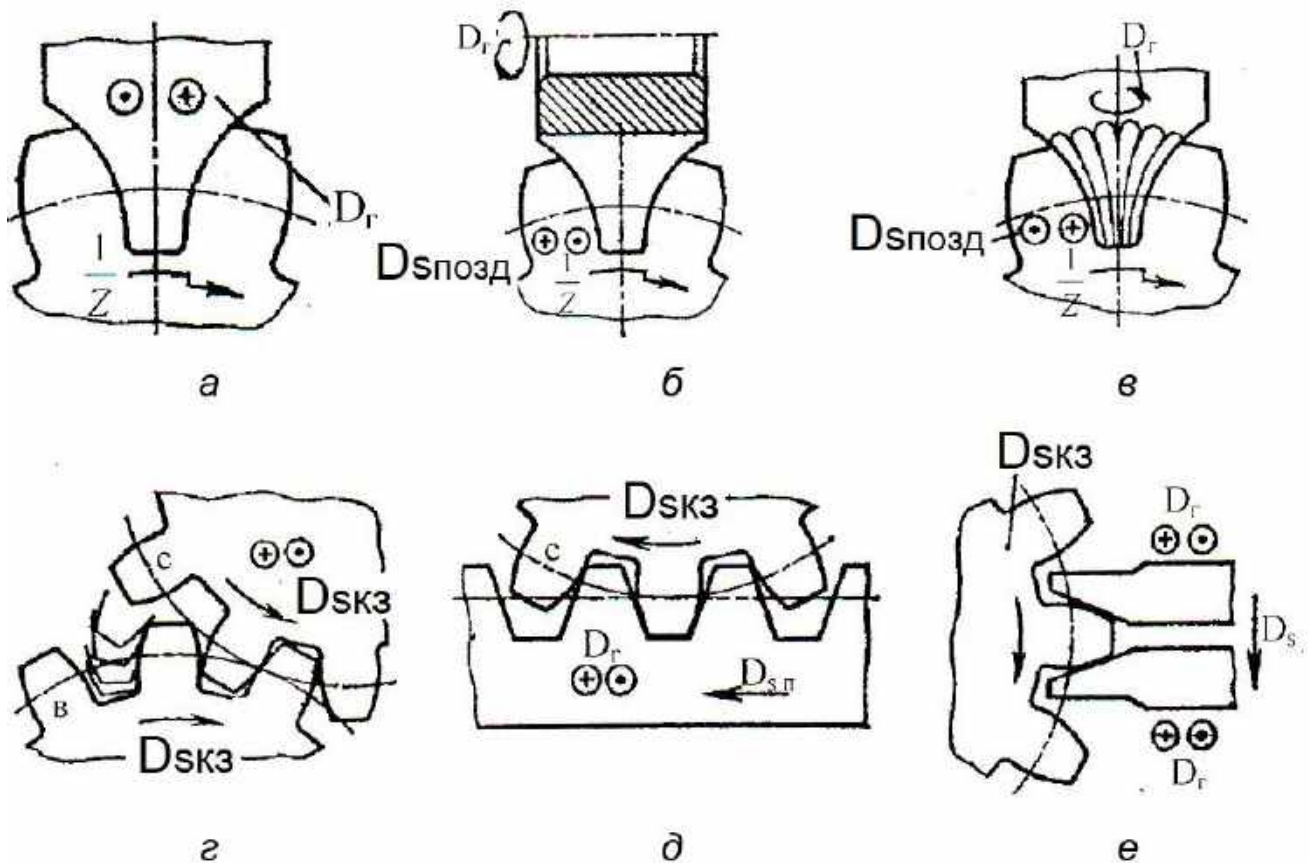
Схема профілювання зубчастих евольвентних поверхонь
